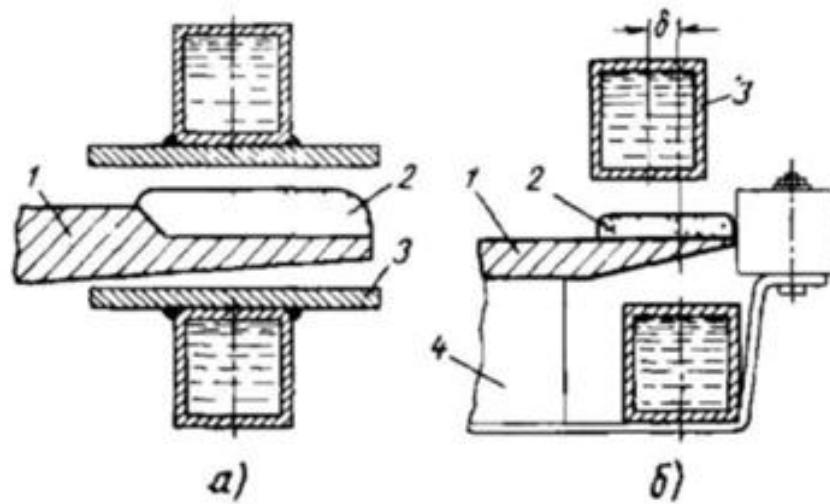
Схема розташування наплавленої деталі в кондуктор
